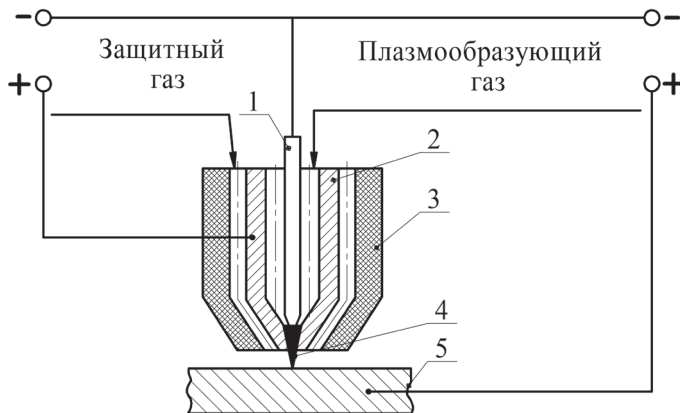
Схема процесса микроплазменной сварки:
